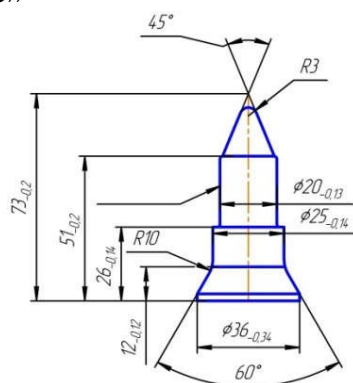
Чертеж детали «Пуансон» №9783-433.09, из номенклатуры
